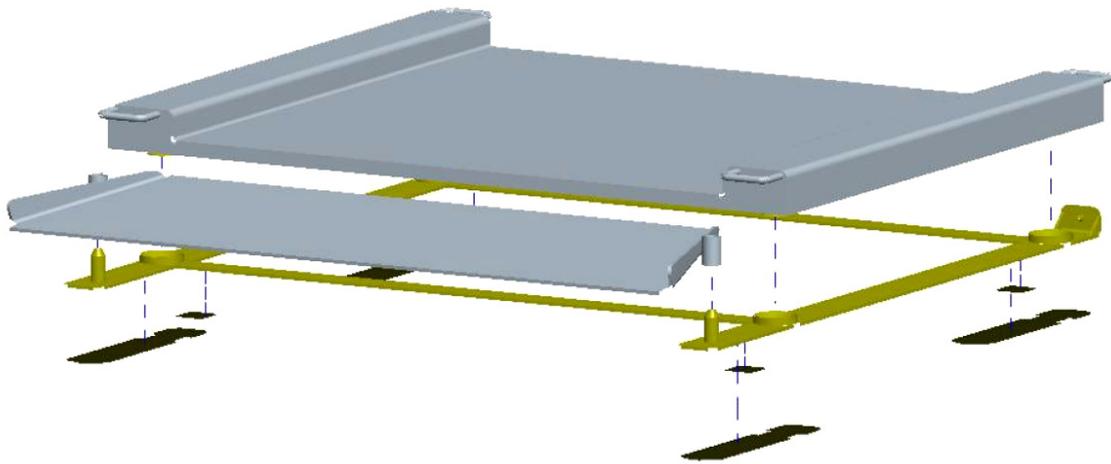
geschlossener Installationsrahmen mit Gummiauflage
